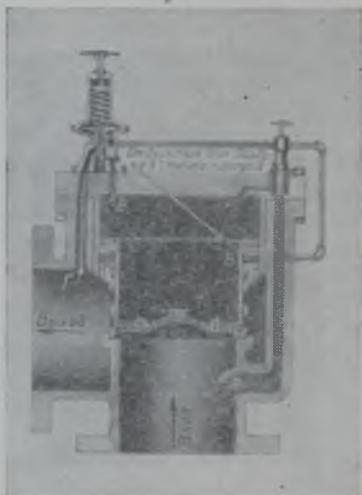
Предохранительный клапан (по материалам Golden-Anderson Valve Specialty Co.)
